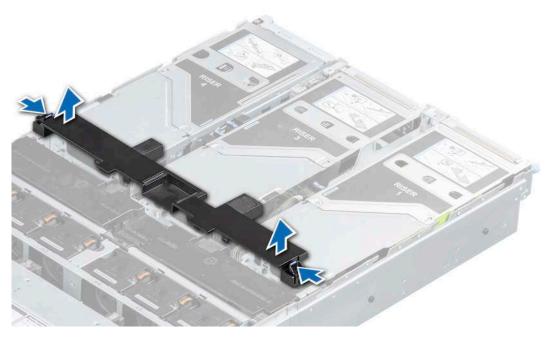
Extracción de la cubierta superior en la cubierta para flujo de aire de la GPU
